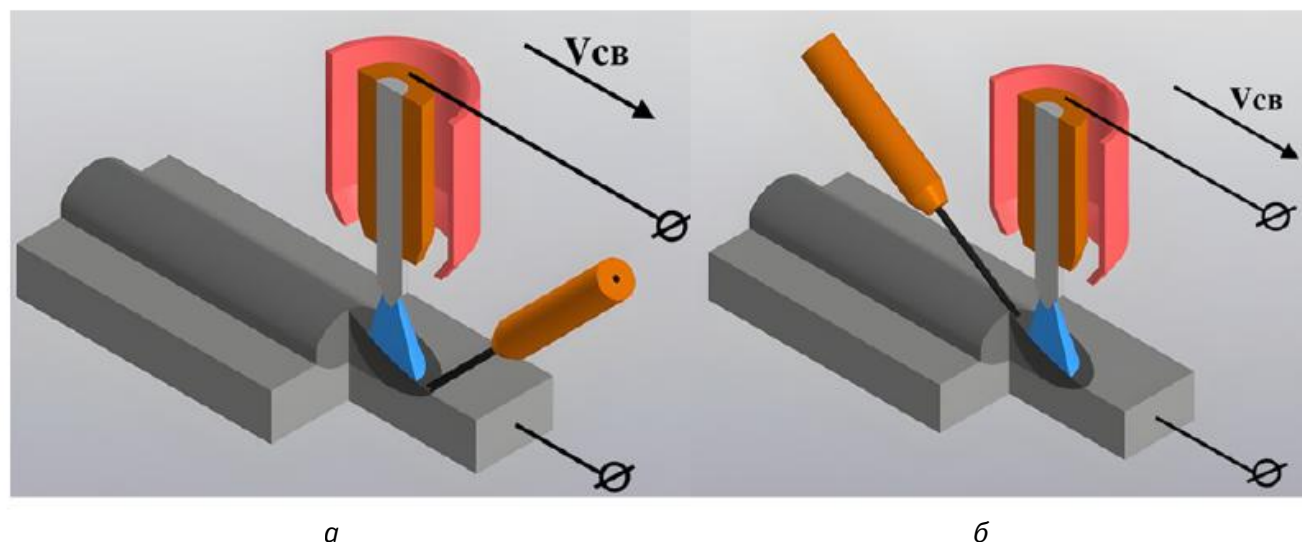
Схемы подачи присадочной проволоки при наплавке неплавящимся электродом: *а* — подача присадочной проволоки по переднему фронту сварочной ванны (схема № 1); *б* — подача присадочной проволоки со стороны хвостовой части сварочной ванны (схема № 2)
